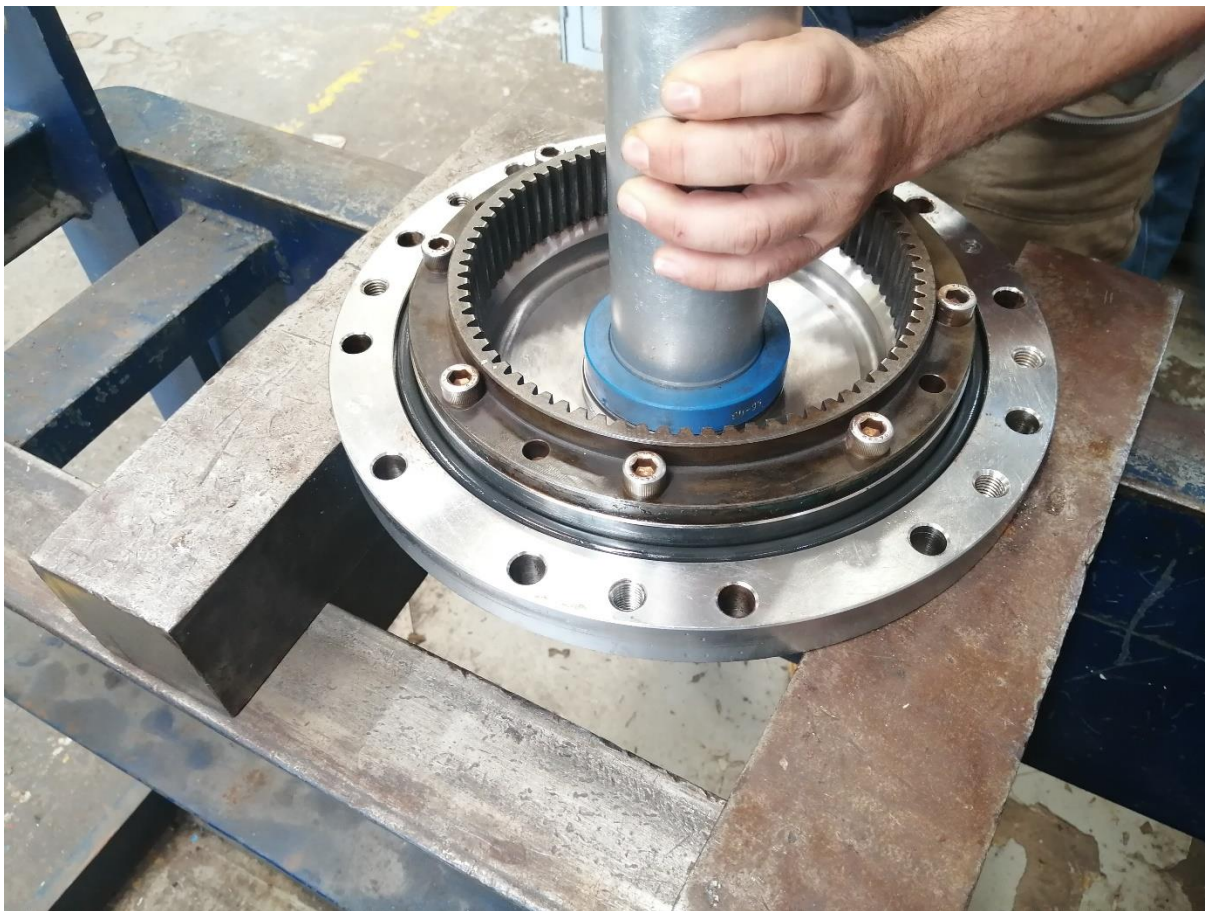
Montaje del rodamiento con el kit para instalar rodamientos
